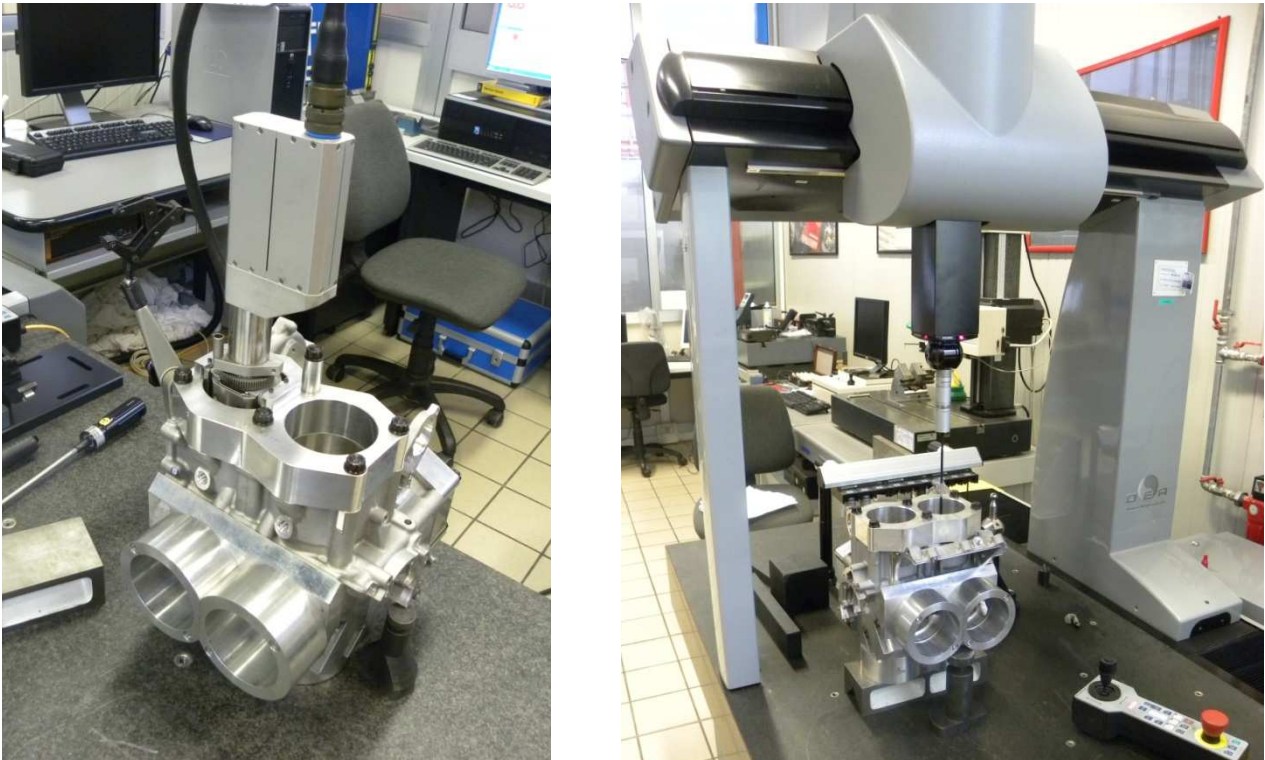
Configurazione BUILD3: torque-plates serrati a 5 Nm, bottom fixture serrato. Incometer a sinistra e DEA a destra
